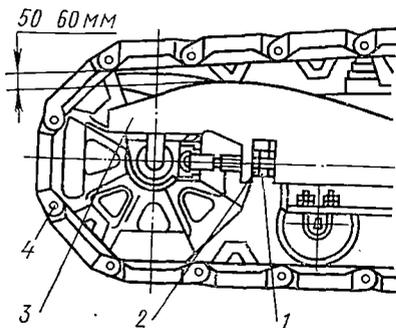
Проверка натяжения гусеничной ленты экскаватора Э-652Б:
